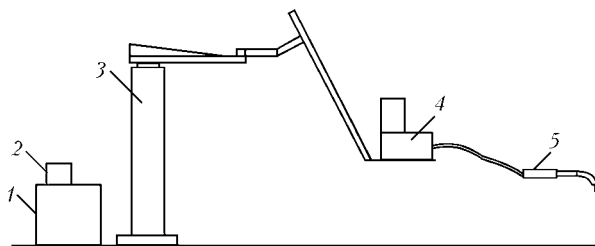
Схема установки для дуговой точечной сварки с проплавлением верхнего элемента: 1 — источник питания; 2 — блок питания механизма полуавтомата; 3 — поворотная консоль; 4 — подающий механизм с электронной системой программирования и управления ДТС; 5 — шланг с держателем
